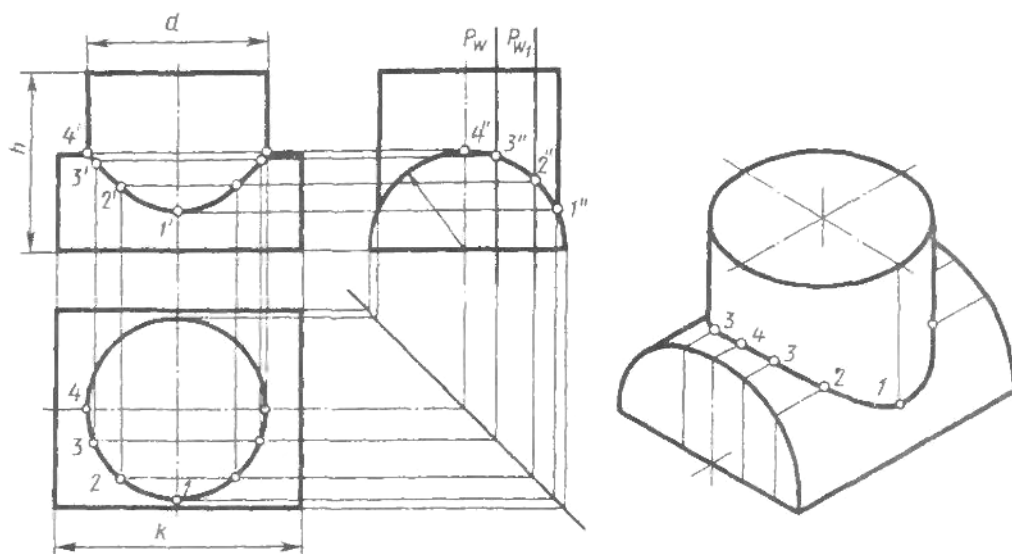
Комплексный чертеж и изометрия пересекающихся цилиндров
